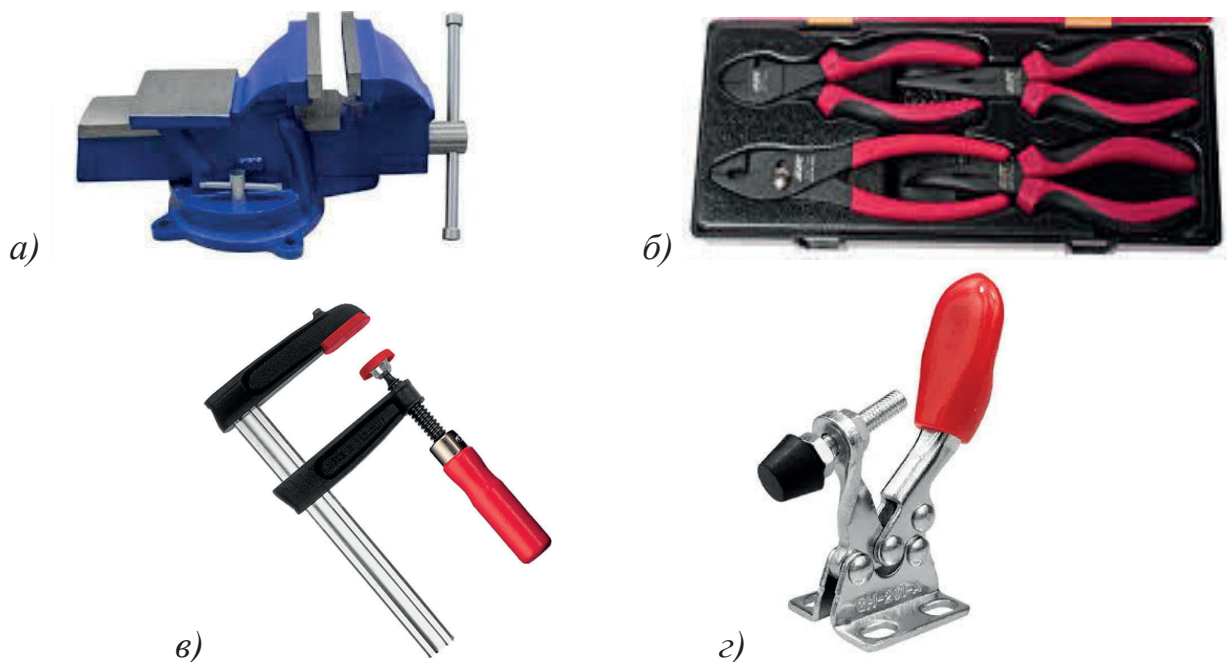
Фіксуючі слюсарні інструменти: а – лещата; б – кліщі; в – струбцина; г – фіксатор
